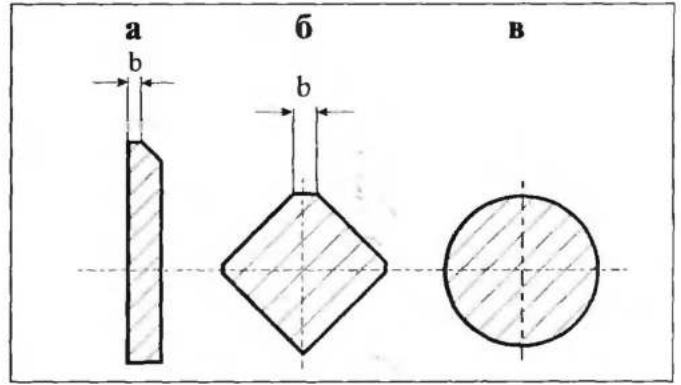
Сечения ножей для параллельных стендов: а — плоский нож; б — призматическая направляющая для деталей весом до 200 кг; в — направляющая круглого сечения для деталей весом 40-50 кг
